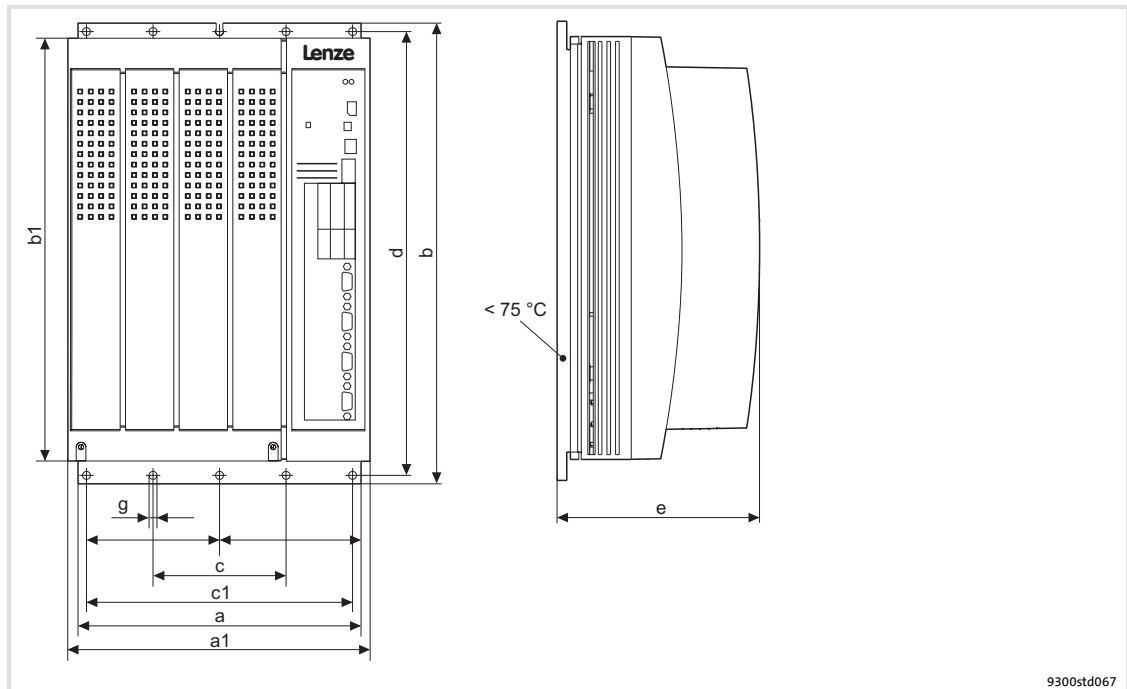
Abmessungen Montage in "Cold Plate"-Technik 15 ... 22 kW
